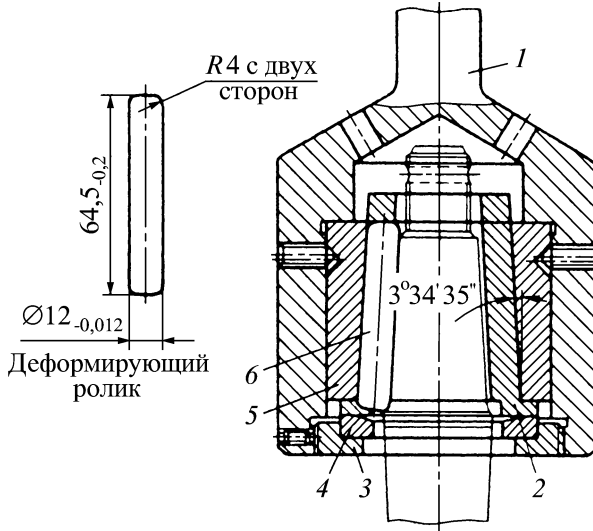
Многороликовый обкатник с цилиндрическими роликами для обработки конических поверхностей:
